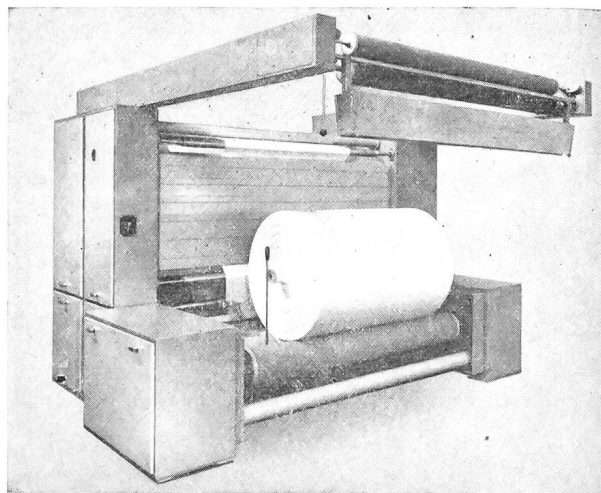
Warenausgangsseite der Gewebeaufbereitungsmaschine IMPERATOR mit Steigdocken-Aufrollvorrichtung für kantengerades Rollen. Die Abbildung zeigt eine Maschine für wahlweises Abtafeln oder Aufrollen der Gewebe.
